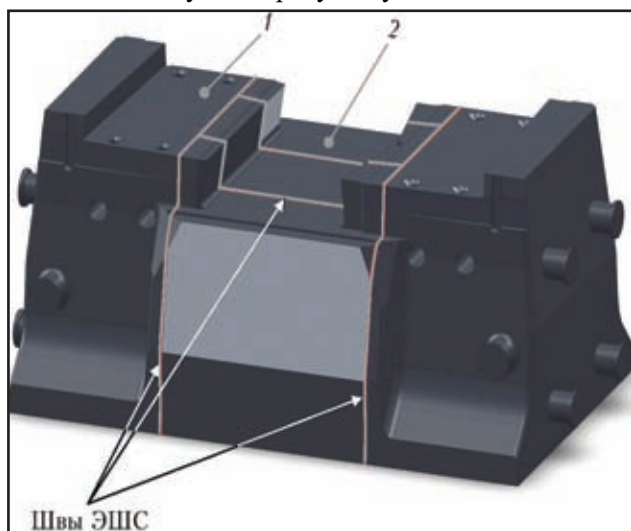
Расположение швов ЭШС при изготовлении шабота: 1 — литые части (сталь 30Л); 2 — ковано-сварная средняя часть шабота, состоящая из трех поволоков из стали ИЦ-1А
